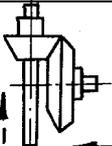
Проверка регулировки подшипников ведущей конической шестерни
